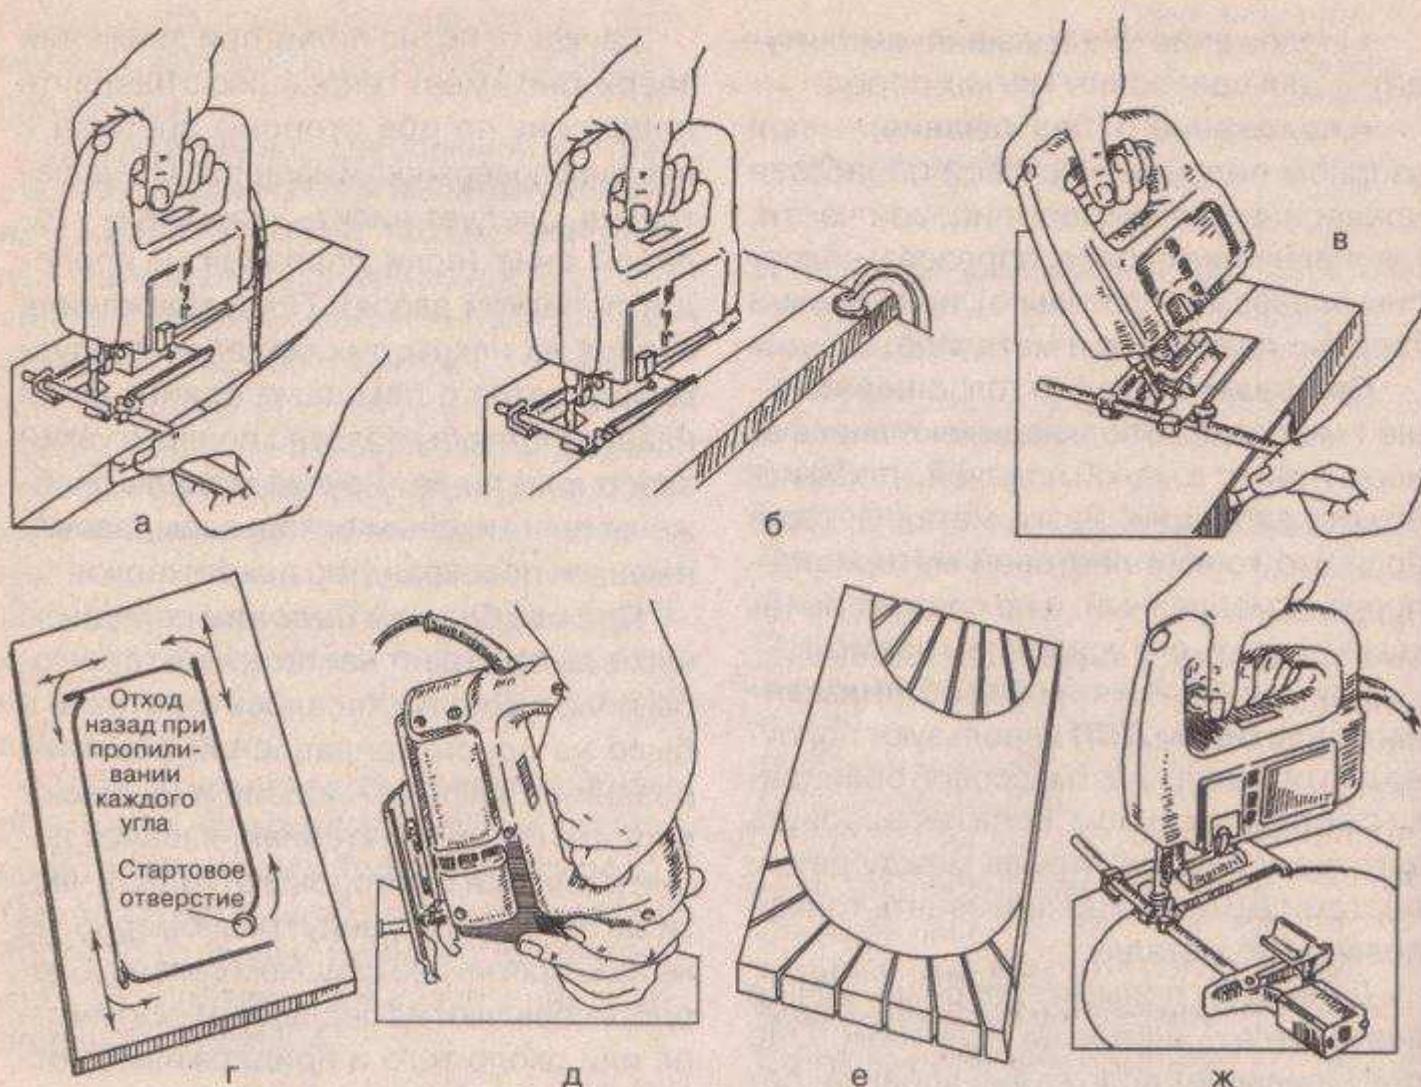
Пиление электролобзиком: а — прижатие линейки к заготовке при параллельном пиления; б — перемещение лыжи вдоль направляющей рейки; в — пиление скоса при помощи линейки; г — выпиливание прямоугольного отверстия; д — начало врезного пиления; е — выполнение криволинейного пиления; ж — выпиливание окружности при помощи линейки и «центрика»
